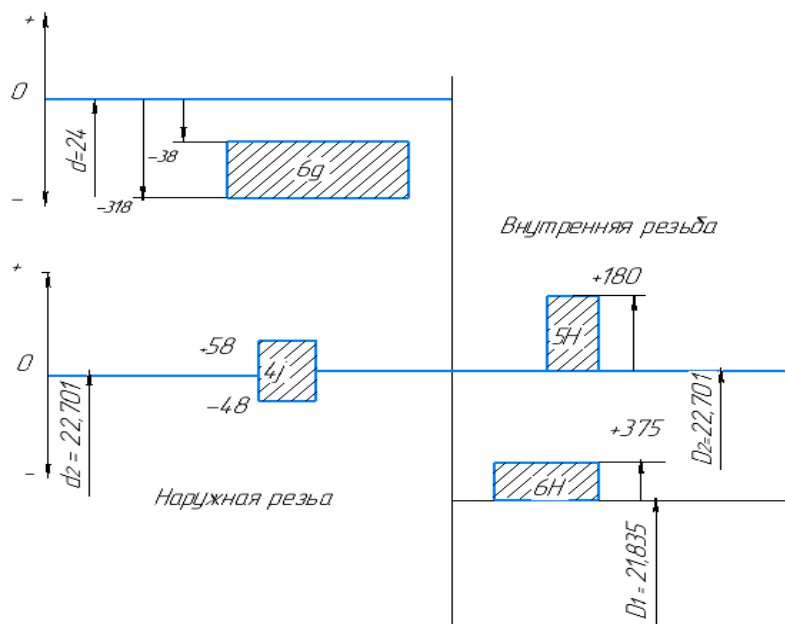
Схема полей допусков резьбового соединения с переходной посадкой
